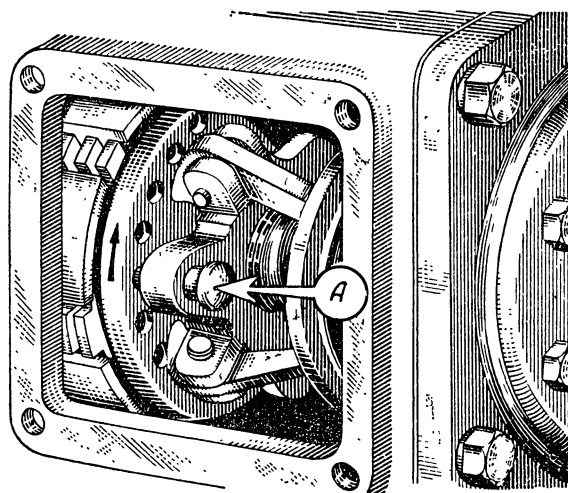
Регулировка муфты сцепления пускового двигателя.
